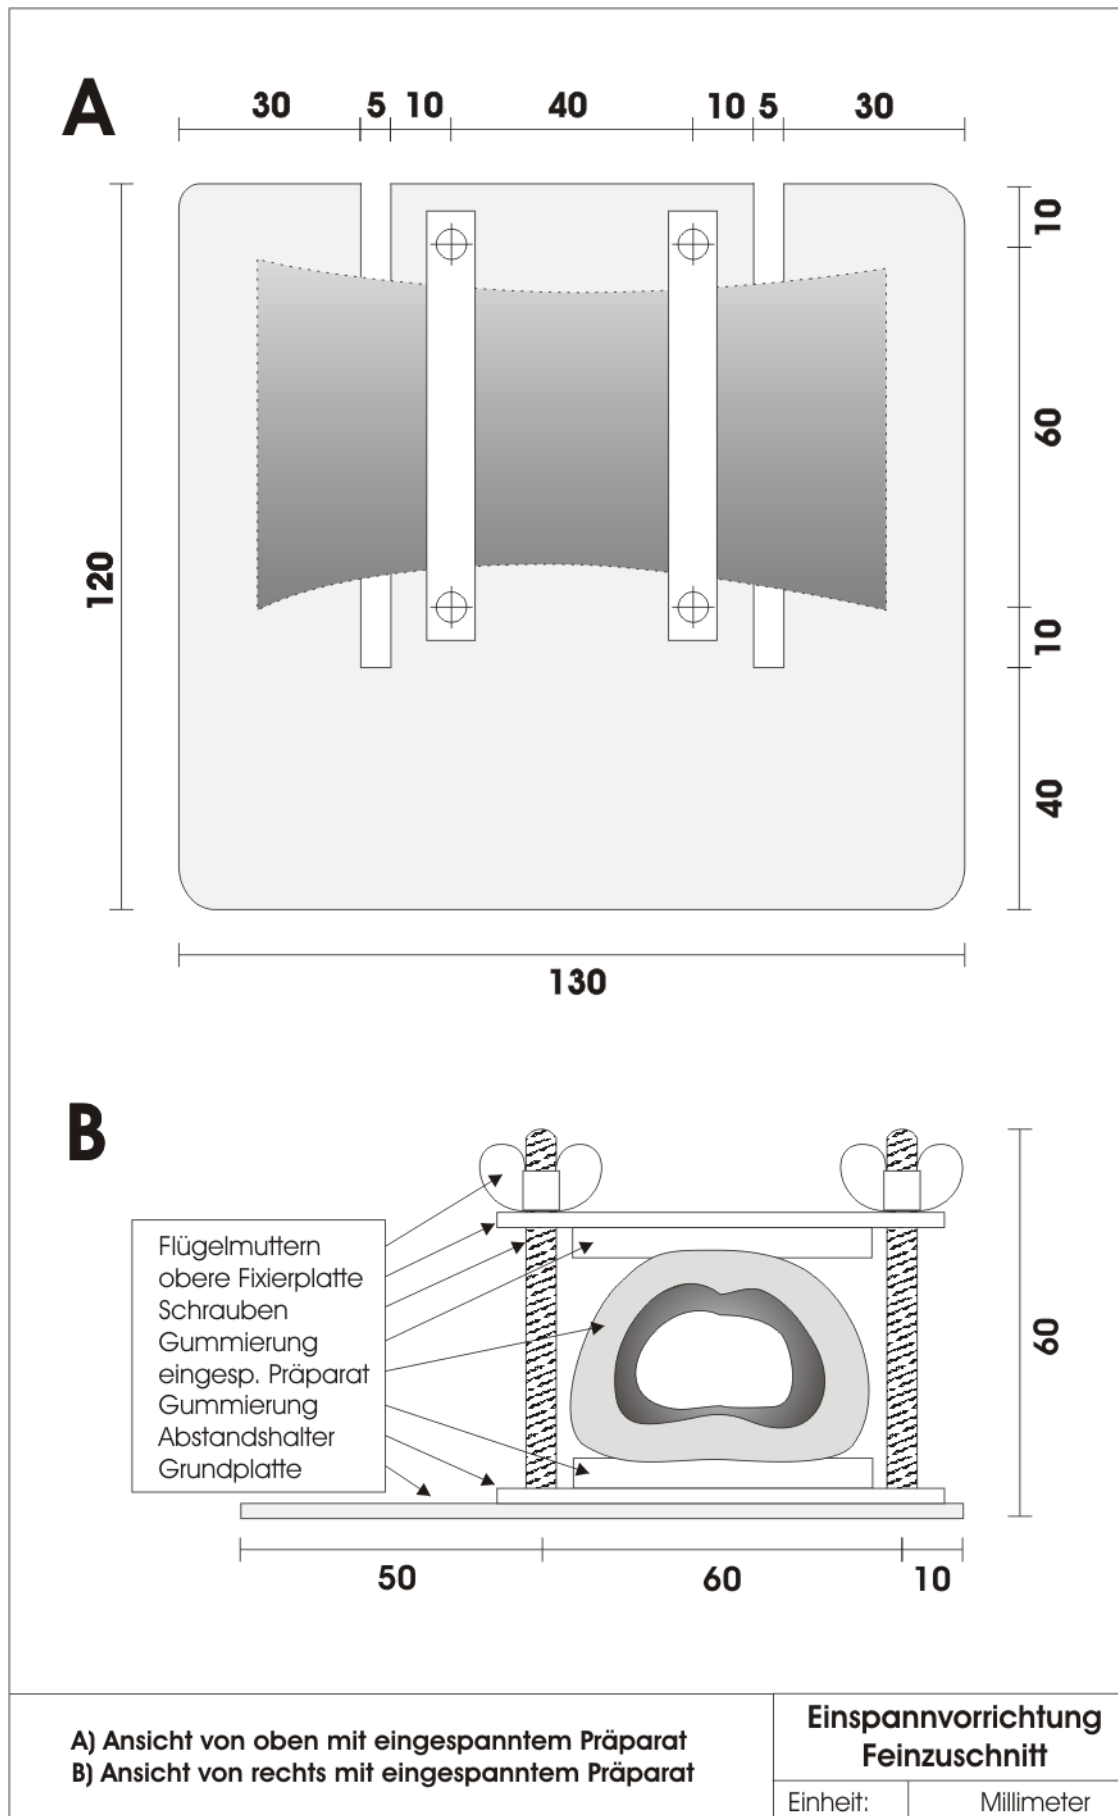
Vorrichtung zum Feinzuschnitt, Risszeichnung
